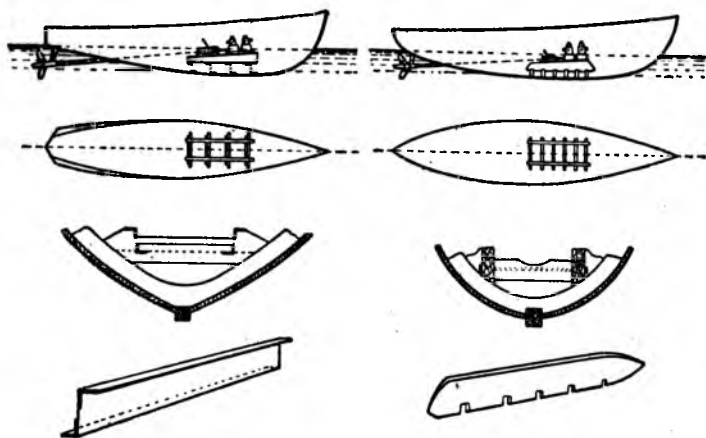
Установка двигателя и передаточных механизмов на фундаменте. Слева — металлический фундамент; справа — деревянный.
